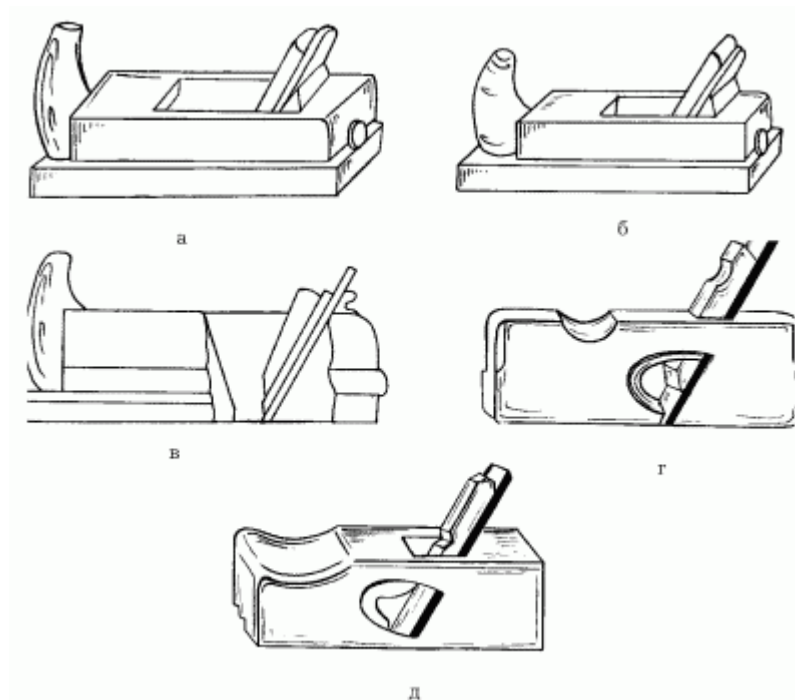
Виды строгальных инструментов: а – шерхебель; б – одинарный рубанок; в – двойной рубанок; г – зензубель; д – фальцгебель.
